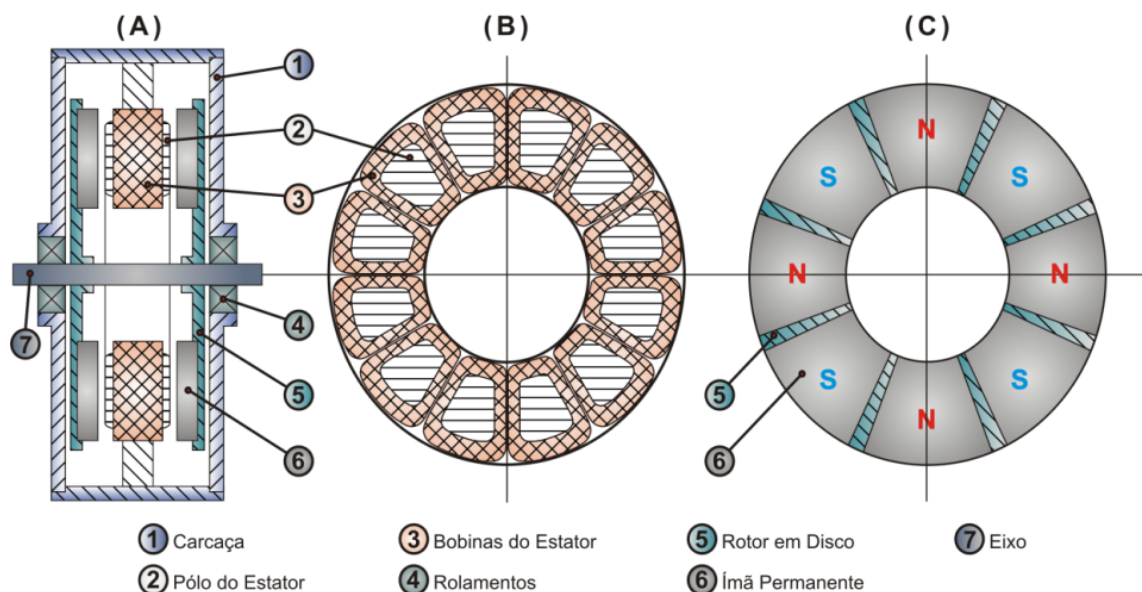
Máquina de fluxo axial de pólos salientes. (A) Estrutura construtiva, (B) vista frontal do estator bobinado, (C) vista frontal do disco de ímãs.
